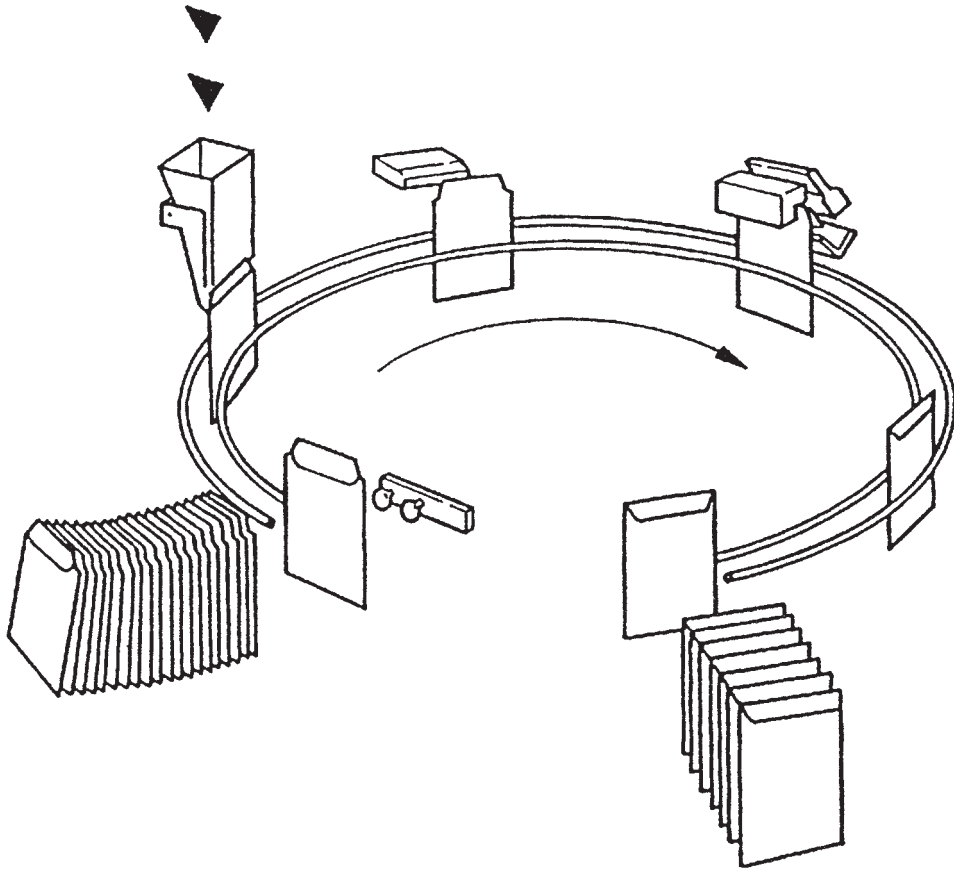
Aufricht-, Füll- und Verschließmaschine für vorgefertigte Beutel
